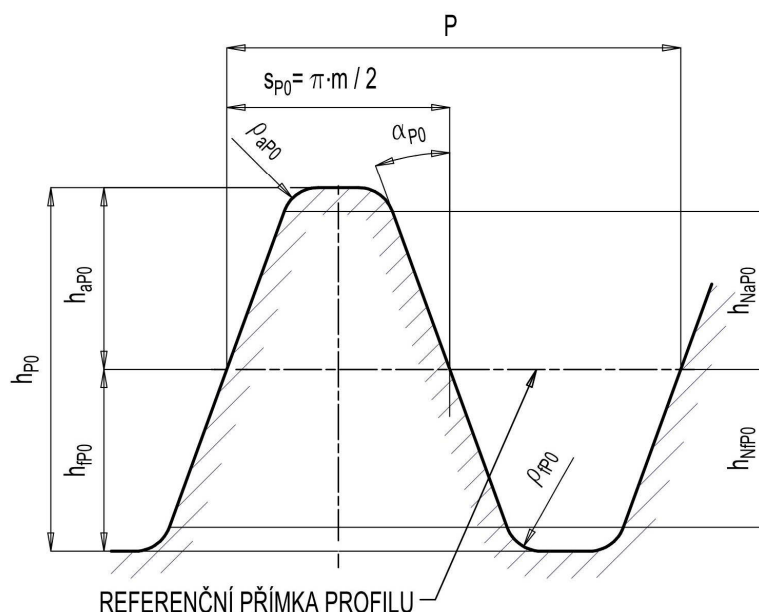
Základní profil ozubení čelního soukolí [3]
